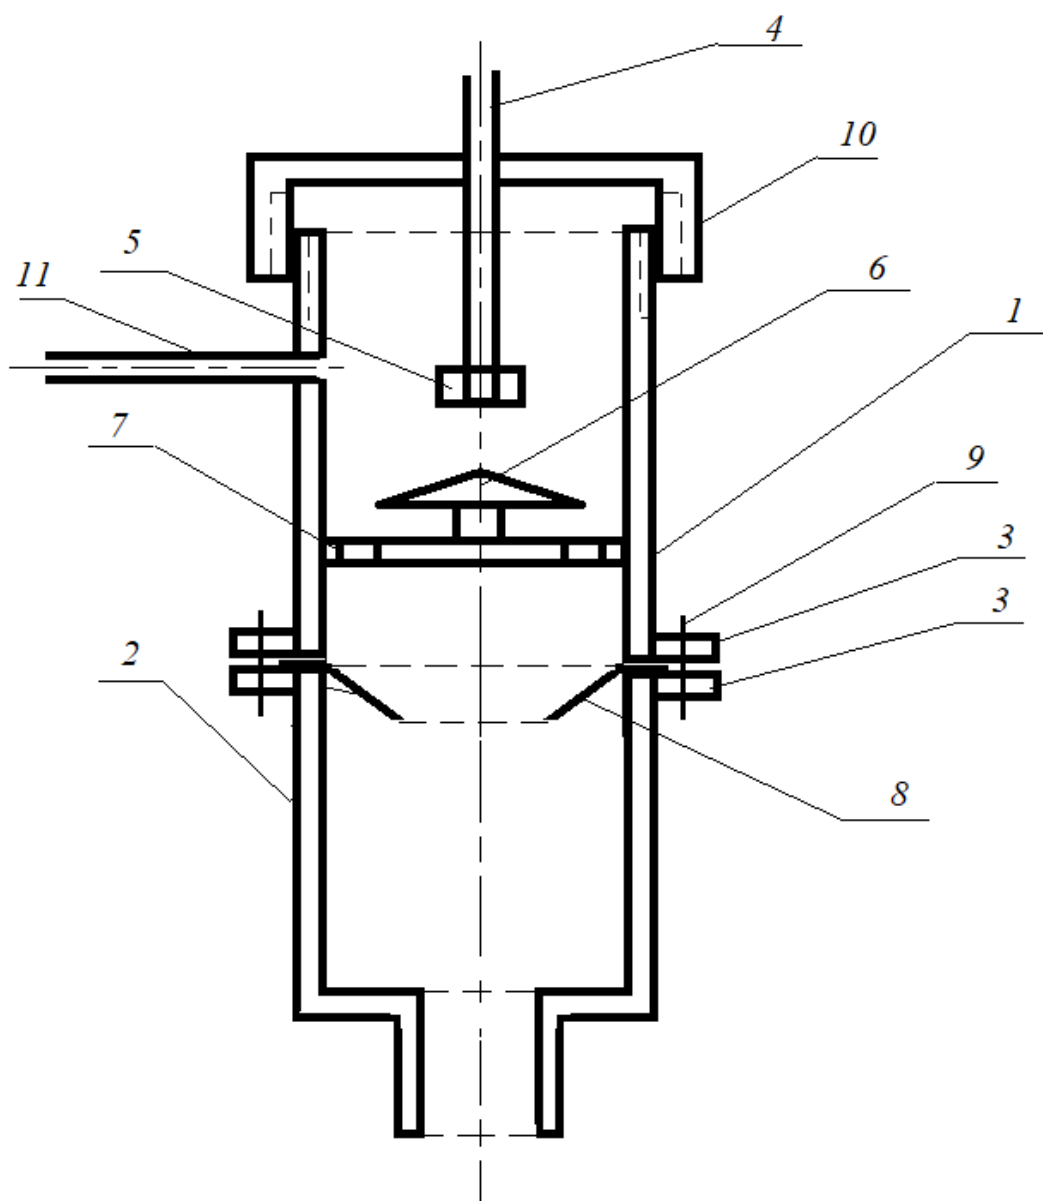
Кавітаційний реактор переробки вуглеводневої сировини в КМП: 1, 2 – верхня та нижня частини реактора; 3 – фланцеве з'єднання; 4 – вхідний патрубок лінії високого тиску; 5 – форсунка; 6 – конусоподібна перегородка; 7 – сітчаста решітка; 8 – дифузор; 9 – шпилька; 10 – кришка; 11 – штуцер
